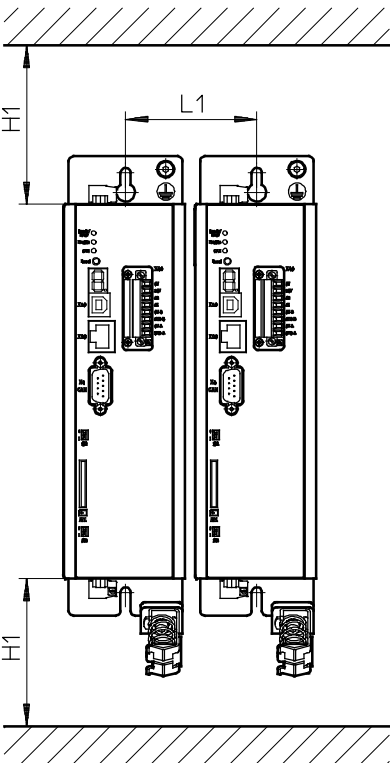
Motorcontroller CMMP-AS-...-M0: Montageabstand und Einbaufreiraum
